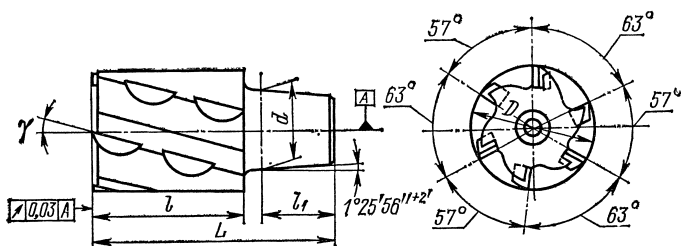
Фреза концевая, оснащенная твердосплавными сегментными пластинами
